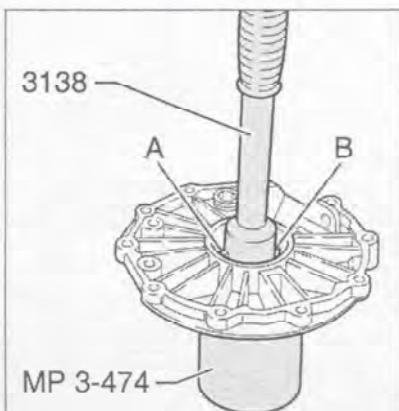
Извлечение наружной обоймы роликоподшипника в крышке.
